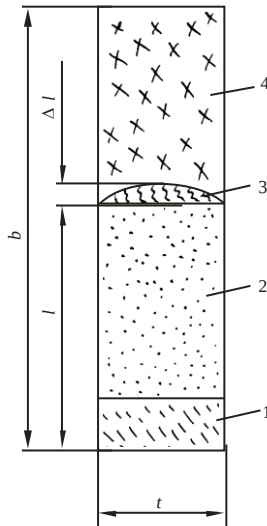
Схема поверхности излома образца при определении J_{1C} . Зоны: 1 – концентратора; 2 – предварительного усталостного разрушения; 3 – вязкого разрушения; 4 – хрупкого долома; b , t – ширина и толщина образца; l , Δl – длина и подрастание трещины.
